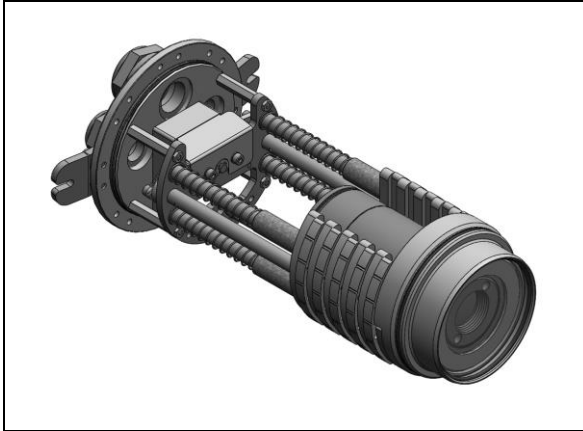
Frontaufsatz mit Pyrometer im Chassis
